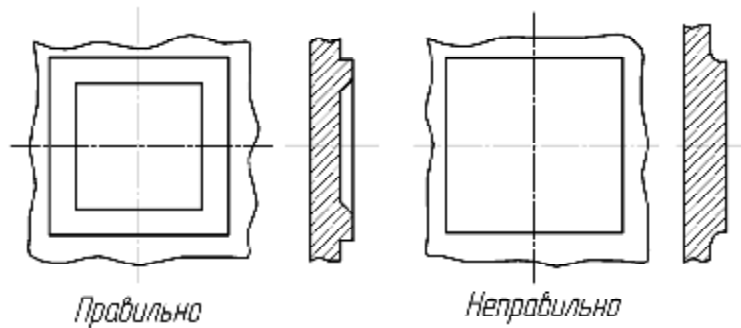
Конструирование литых деталей с обрабатываемыми поверхностями
